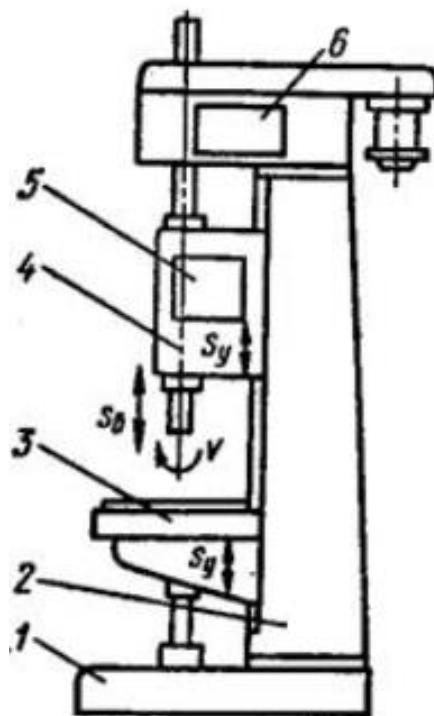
Типове компонування вертикально-свердлильного верстата
